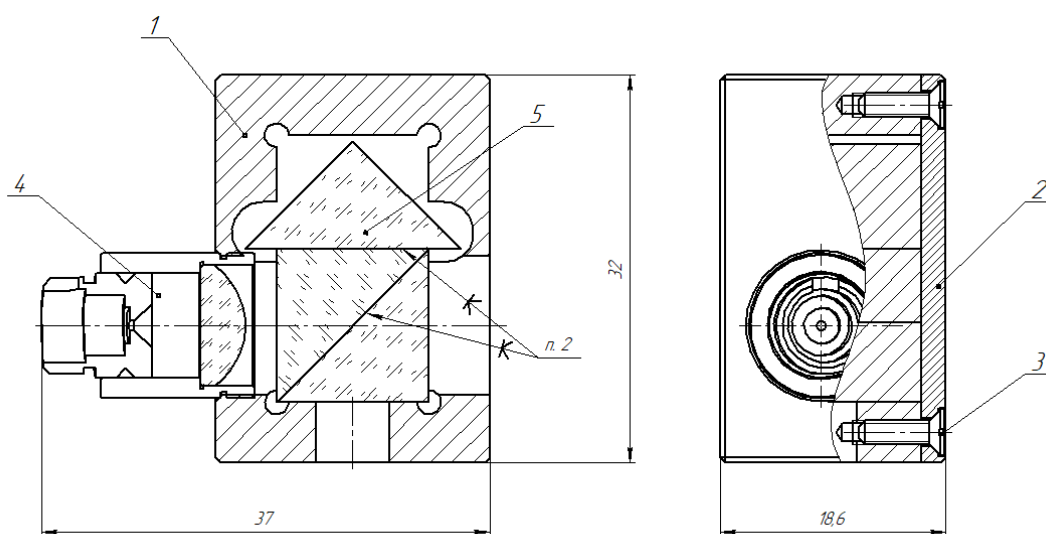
Сборочный чертеж блока интерферометра
